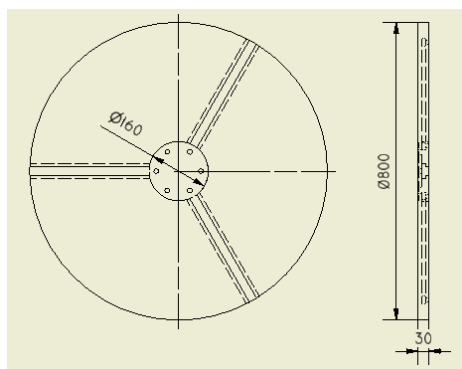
Dimensiones generales del plato soporte de la coquilla
